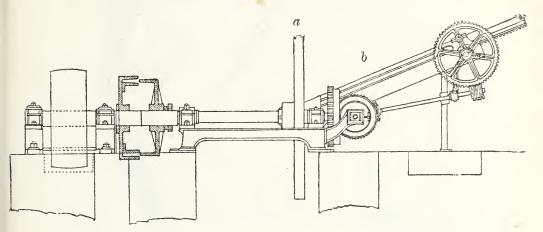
Englische Maschine zum Zerkleinern der Farbhölzer.
